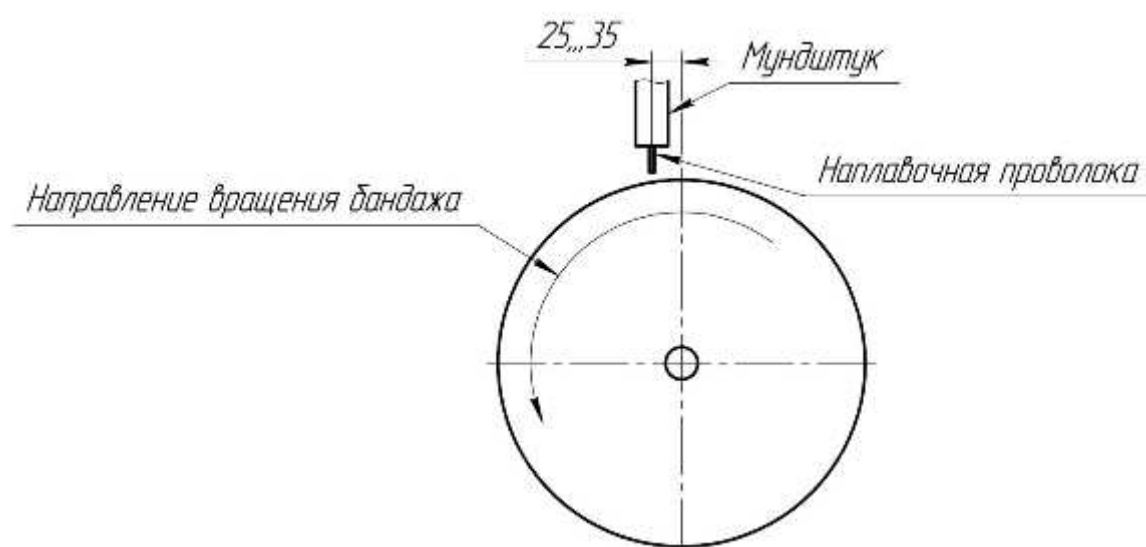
Схема расположения наплавочной проволоки относительно наплавляемой поверхности
